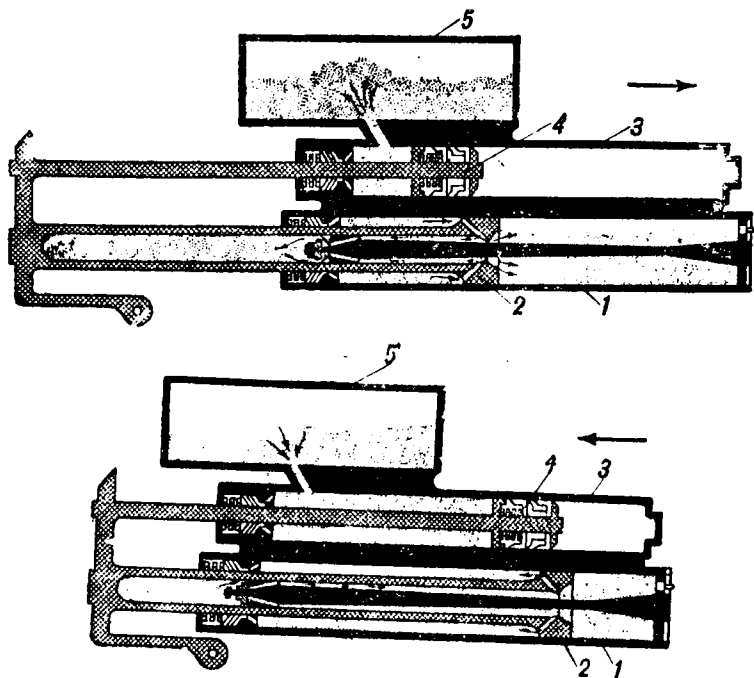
Схема гидравлического тормоза отката и пневматического накатника орудия. Вверху — момент отката; внизу — момент наката. 1 — цилиндр тормоза; 2 — поршень тормоза; 3 — цилиндр накатника; 4 — поршень накатника; 5 — воздушный резервуар.
